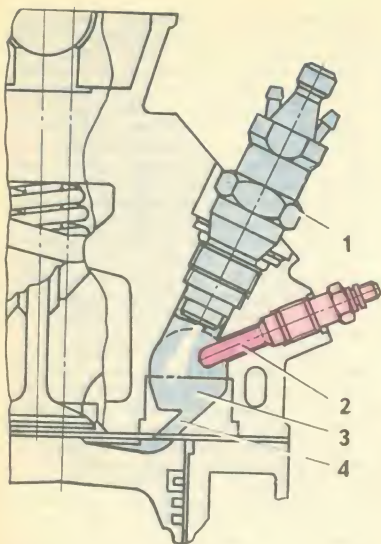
Установка свечи накалывания: 1 — форсунка; 2 — свеча; 3 — вихревая камера; 4 — соединительный канал.
